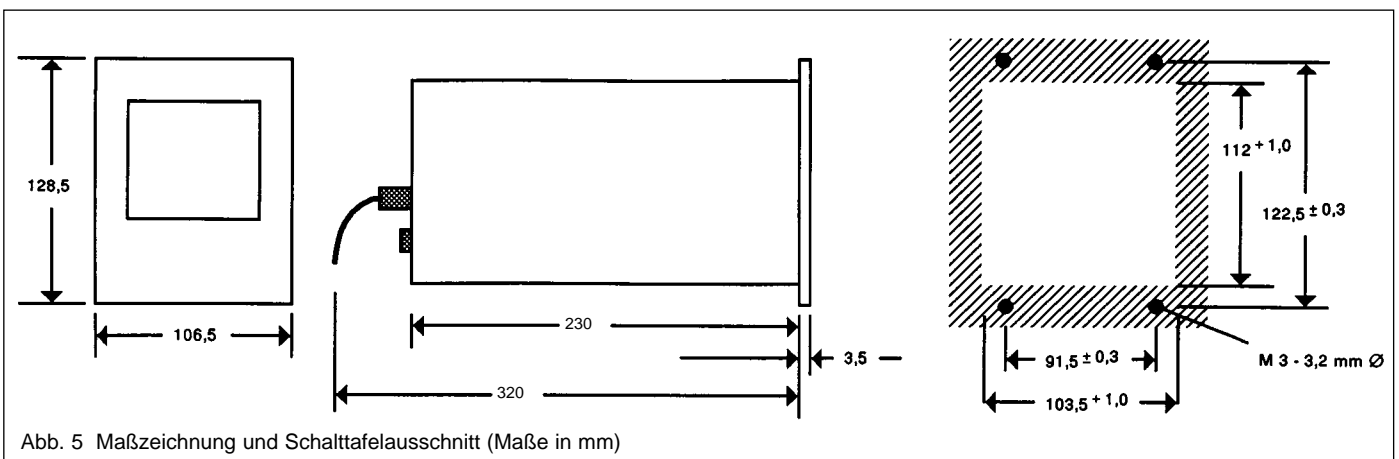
Maßzeichnung und Schalttafelausschnitt (Maße in mm)
